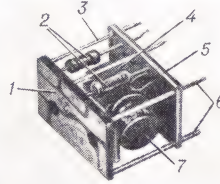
Объёмный модуль (без кожуха) — усилитель звуковой частоты: 1 — верхняя печатная плата; 2 — резисторы; 3 — металлическая перемычка между печатными платами; 4 — конденсатор; 5 — нижняя печатная плата; 6 — выводы; 7 — транзистор.
